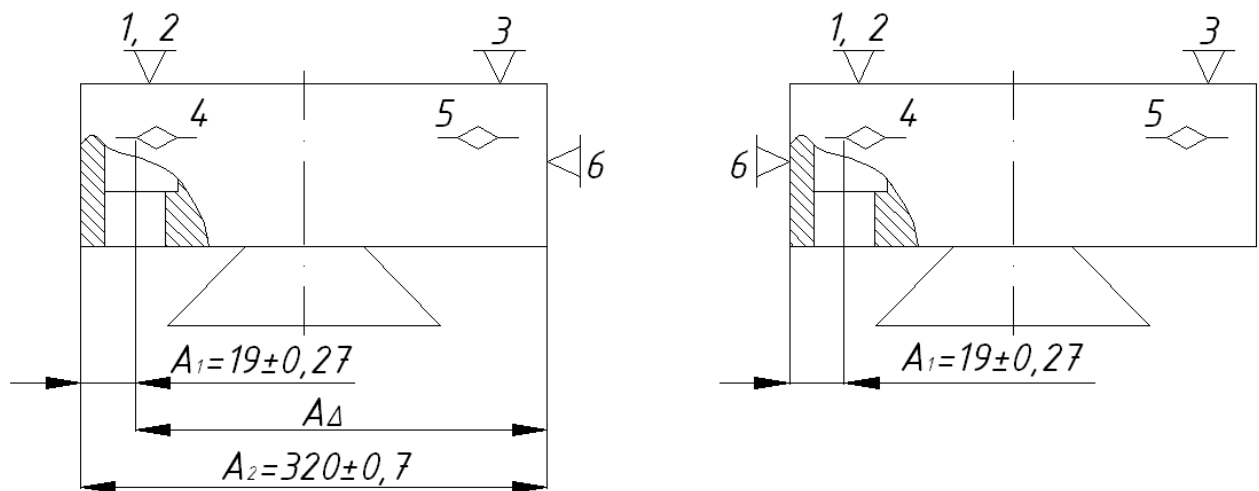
Теоретична схема базування при обробленні шпонкового паза 16
